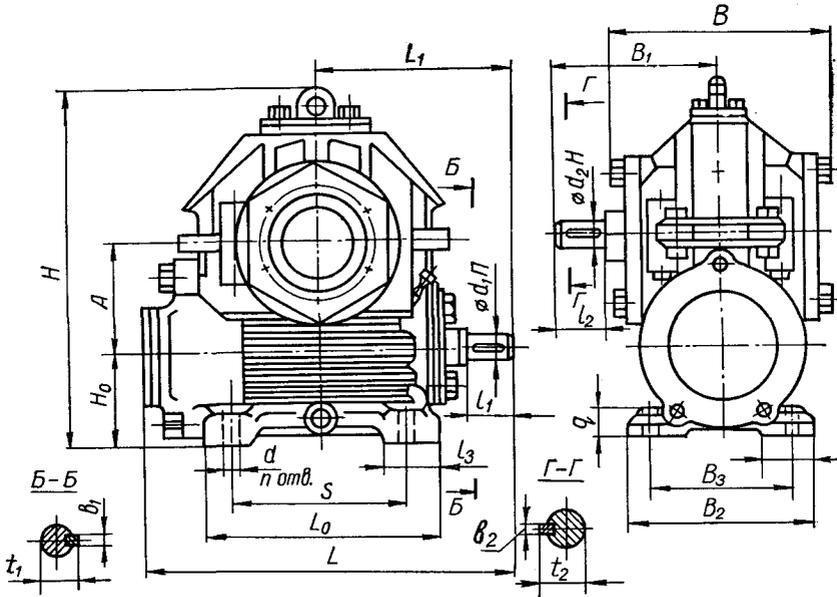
Основные и габаритные размеры редукторов РЧП-300 и РЧП-420. Редукторы с вентиляторами.
